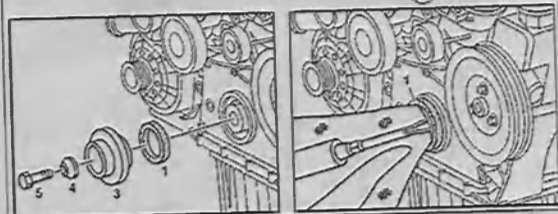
Установка и снятие устройства для блокировки коленчатого вала.
